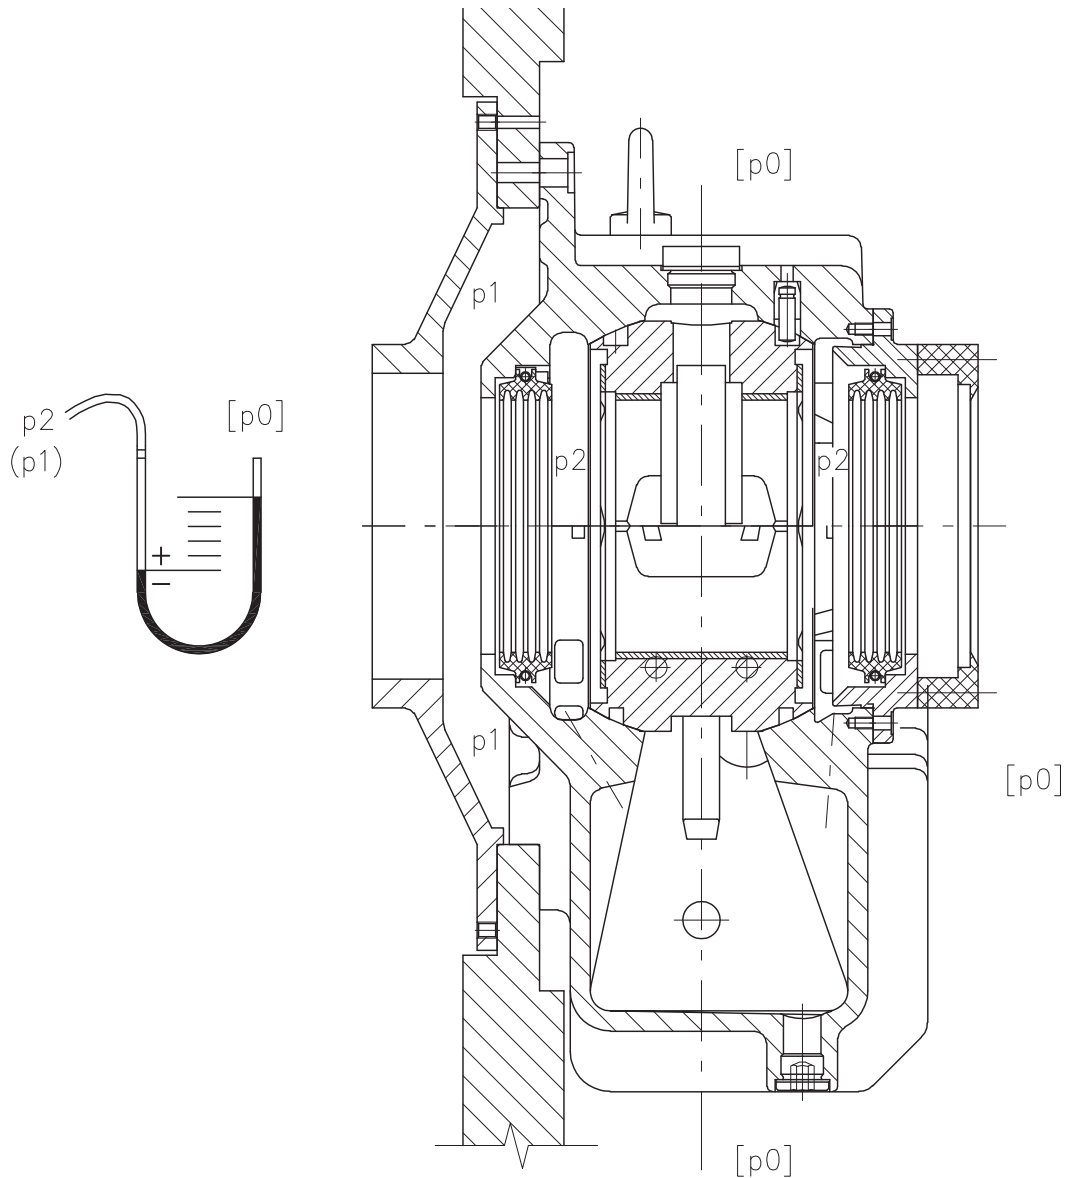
Проверка давления воздуха внутри и вне подшипника скольжения
